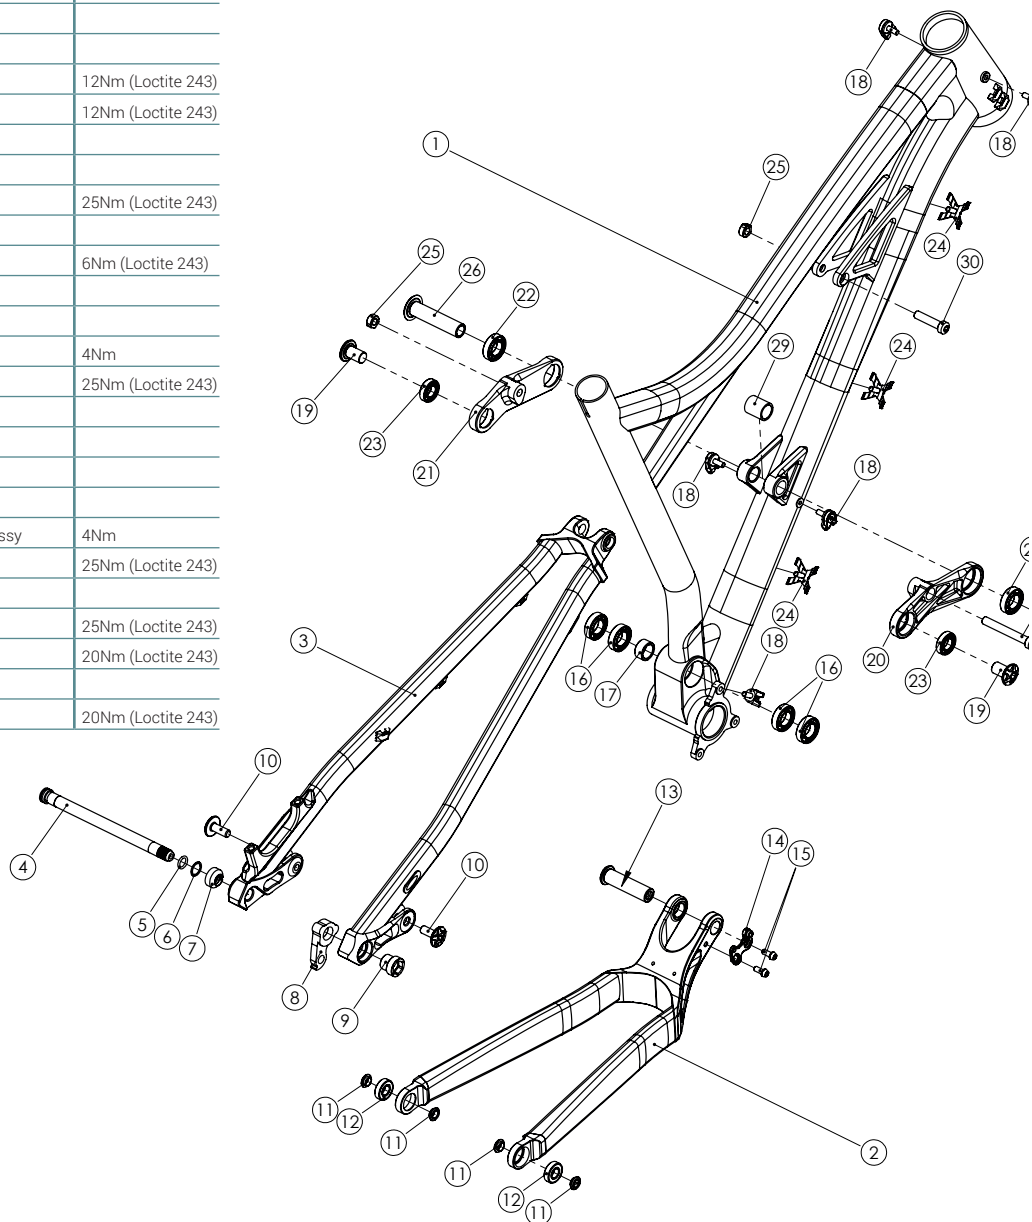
edison EVO Explosionszeichnung mit Anzugsmomenten
